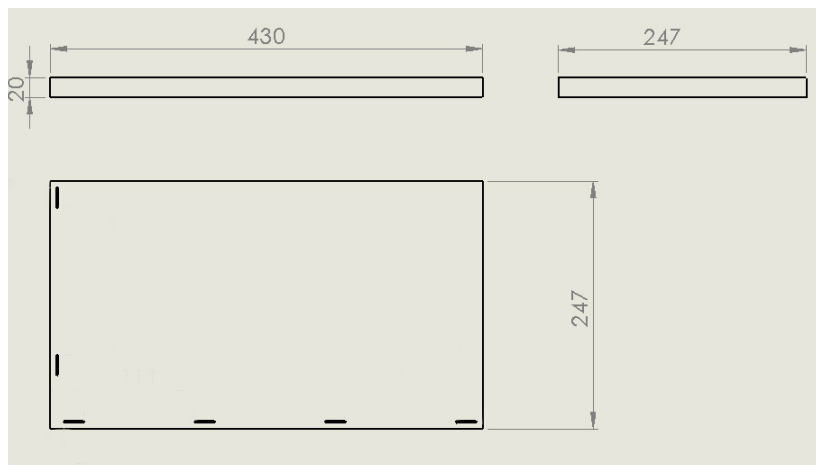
Desenho técnico da placa de 430 x 247 x 20 mm
